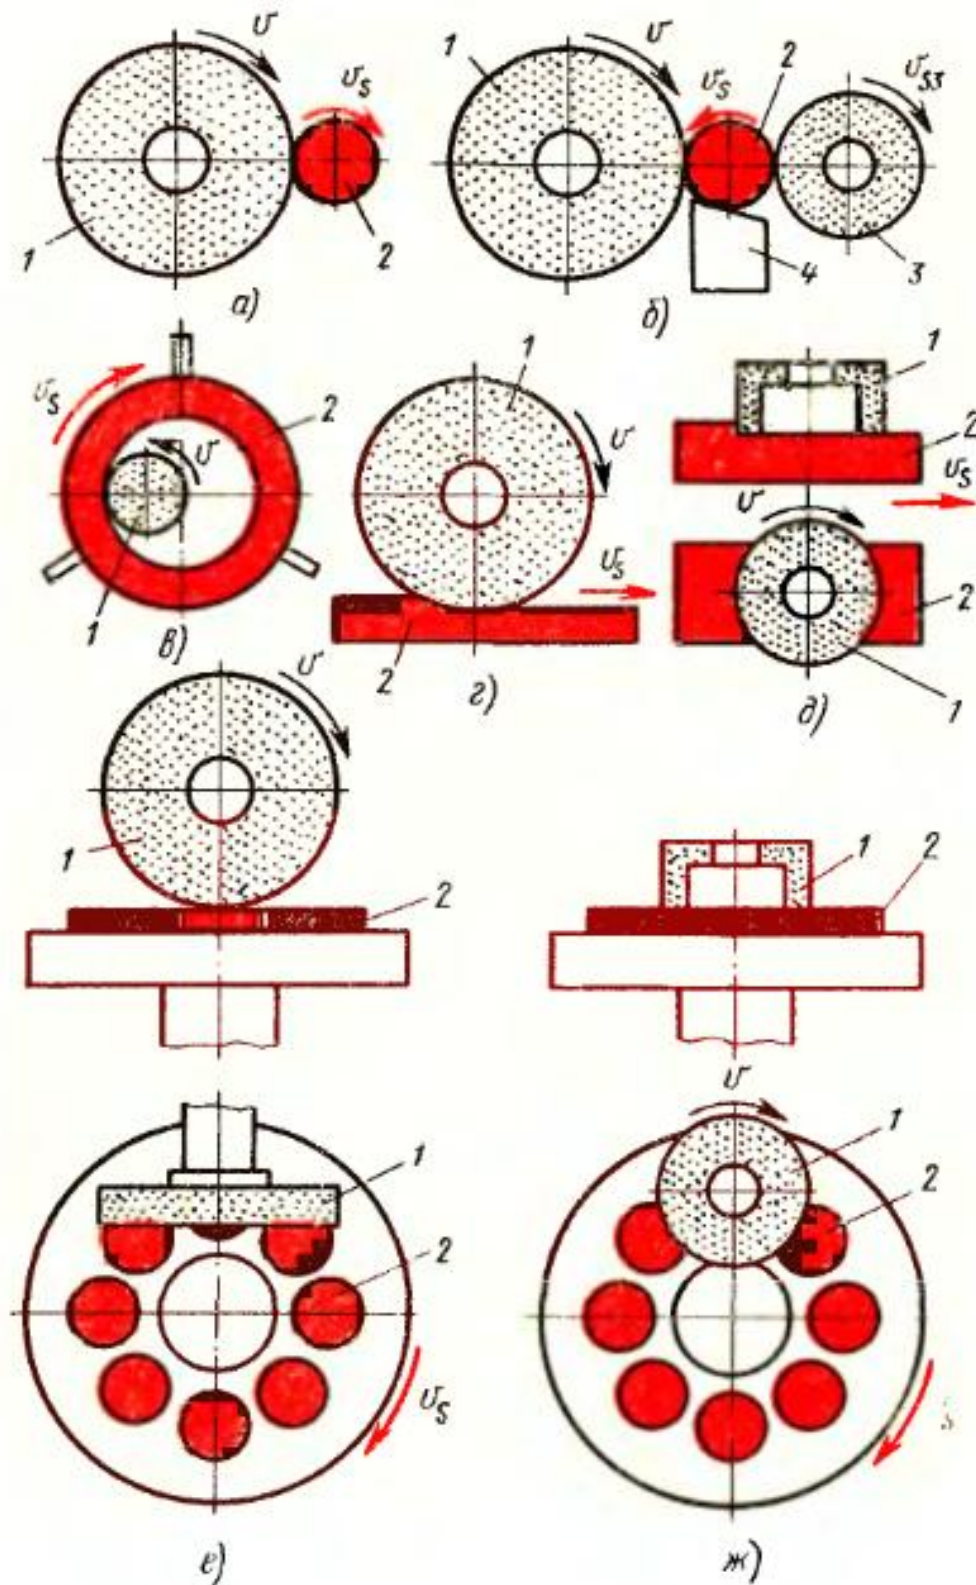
Схемы расположения круга и заготовки и направления движения подачи при шлифовании периферией круга (а, б, е, г, е) и торцом круга (д, ж):
